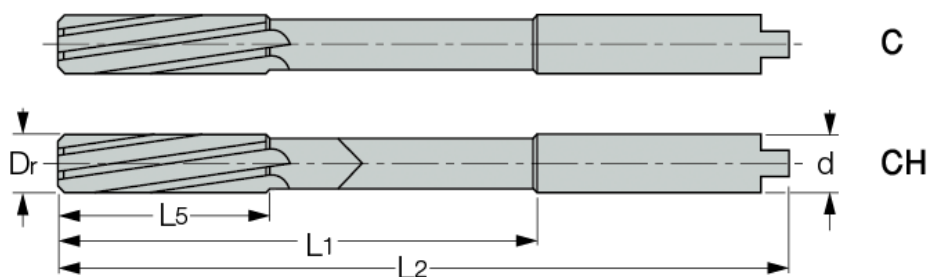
Корпус развертки RM-SHR-0400-H7N-CS-C
